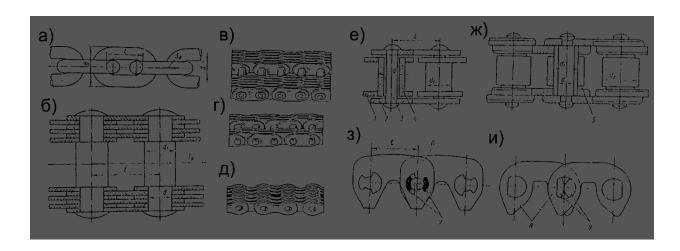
Цепи, применяемые в погрузочно-разгрузочных машинах и механизмах: а - сварная; б - пластинчатая с расклепкой на пластинах; в - пластинчатая с раклепкой на шайбах; г - пластинчатая на шплинтах; д - пластинчатая с закрытыми валиками; е - пластинчатая втулочная; ж - пластинчатая втулочно-роликовая; з - пластинчатая зубчатая с шарниром скольжения; и - пластинчатая зубчатая с шарниром качения.
